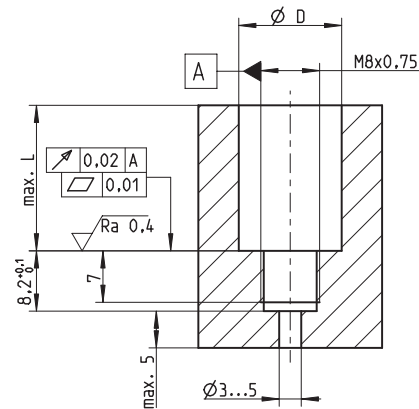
Einbau zurückversetzt. Bohrung $\varnothing$ gemäß Werkzeug Bild 5 oder Bild 6
